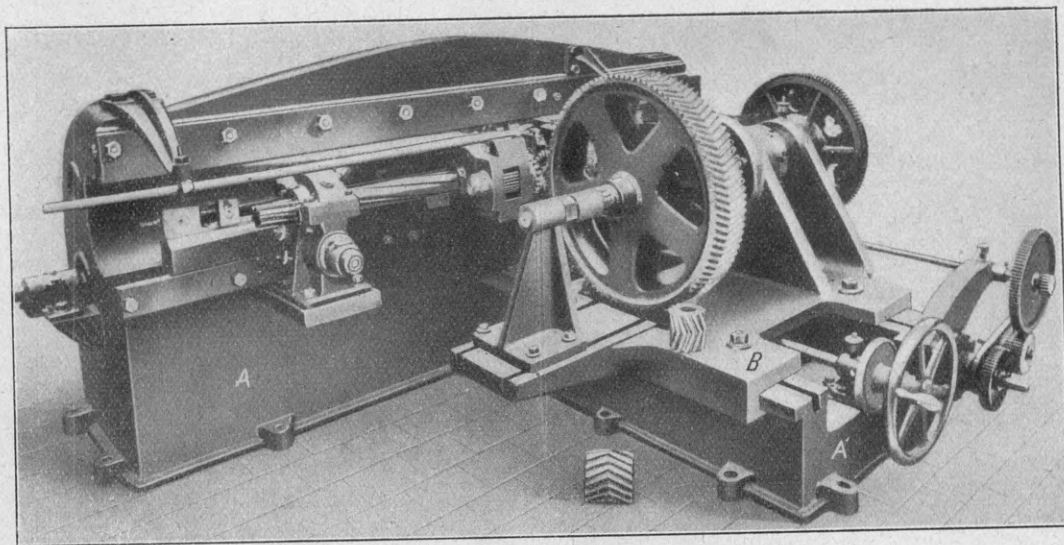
Ansicht der Maschine von der Werkstückseite.
